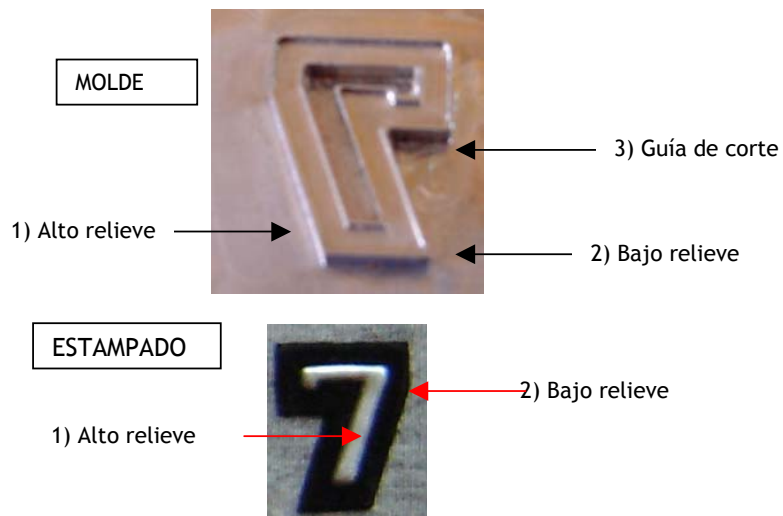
Alto y bajo relieve con guía de corte del molde.
